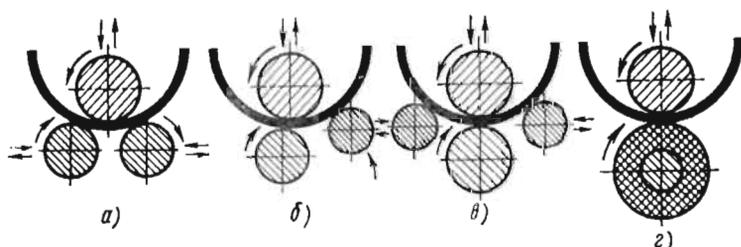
Схемы движений рабочих органов валковых гибочных станков различных типов
